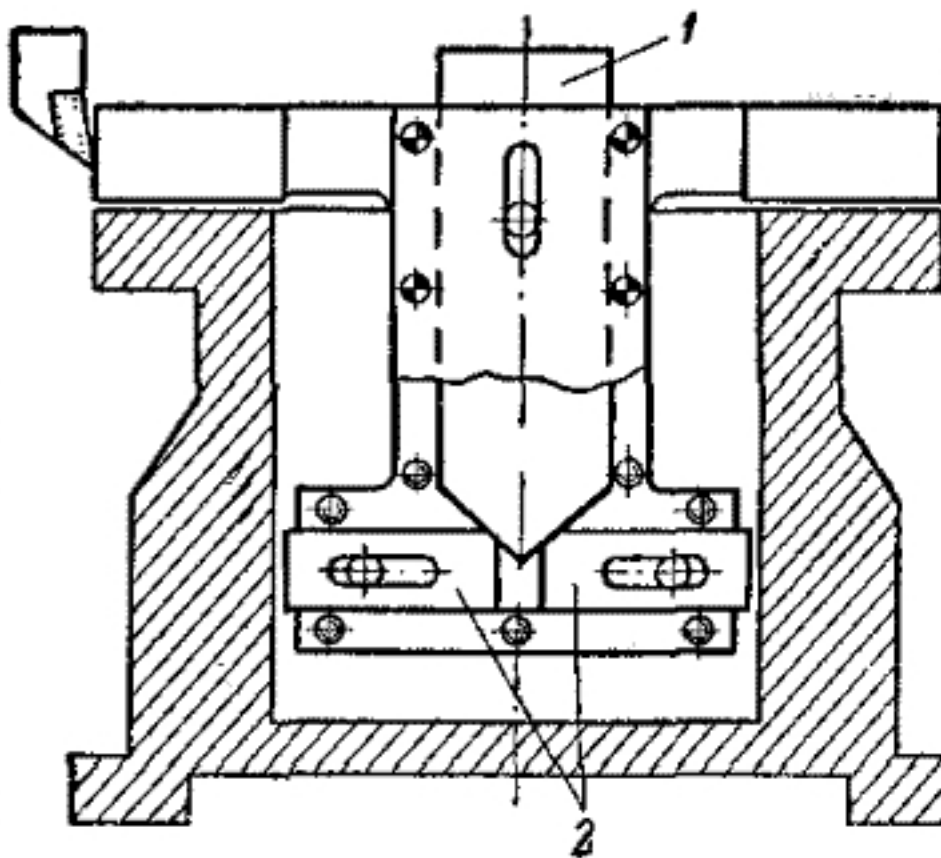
Универсальный раздвижной инструмент для нахождения центра детали.
